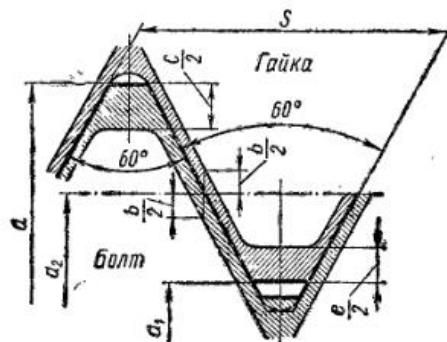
Схема расположения полей допусков метрических резьб:
